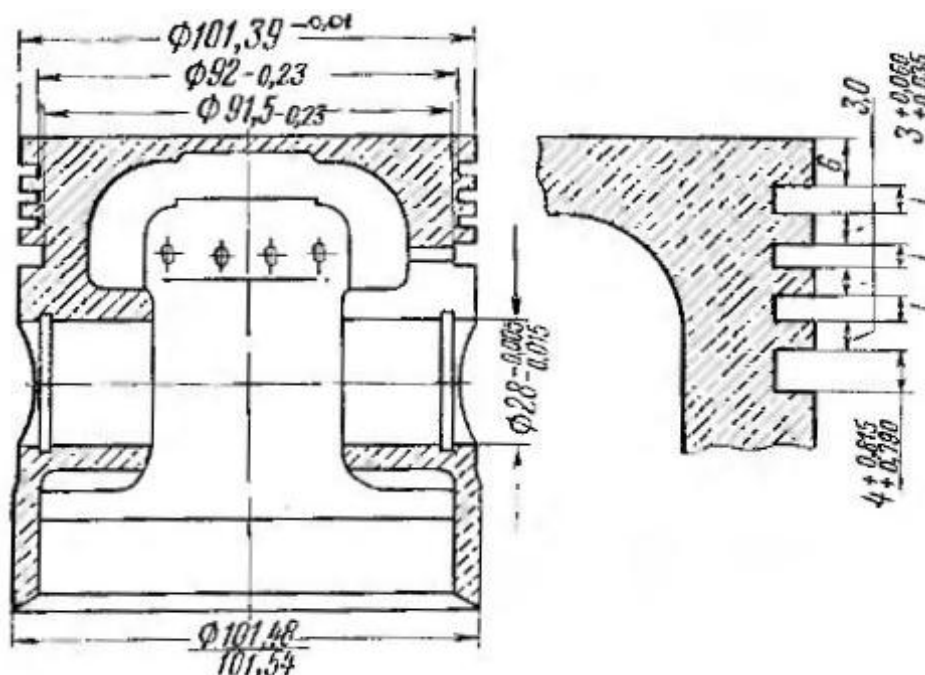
Чертёж поршня двигателя ЗИЛ-508.10.
